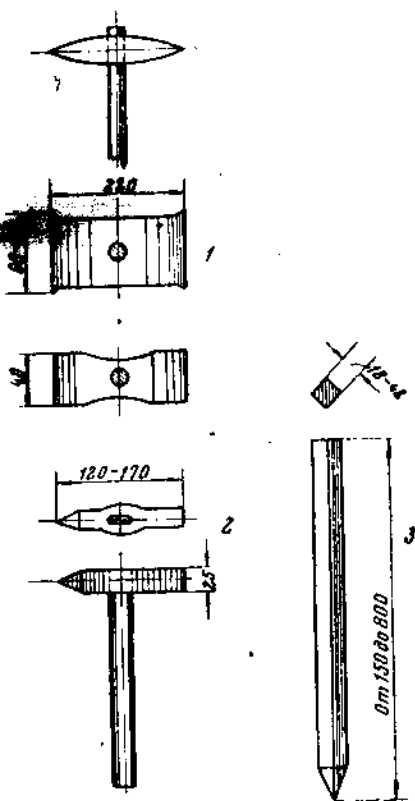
Кирки: 1 — кирка для устройства бороздок; 2 — кирка с рукоятью; 3 — кирка без рукояти
